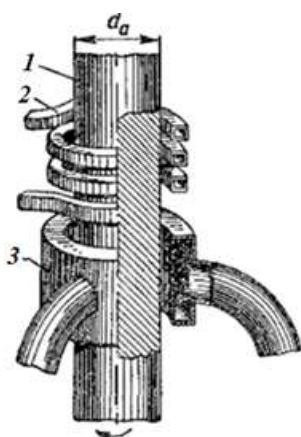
Схема взаимного расположения индуктора и спейнера при закалке детали: 1 - вал; 2 - индуктор; 3 - спрейер;
